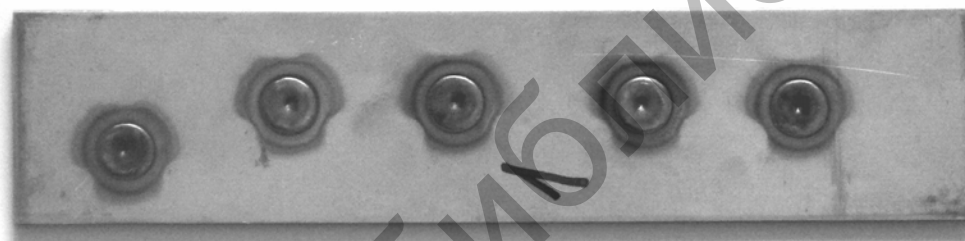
Внешний вид заготовки сварного соединения нержавеющей стали 12Х18Н10Т (вид сверху)
